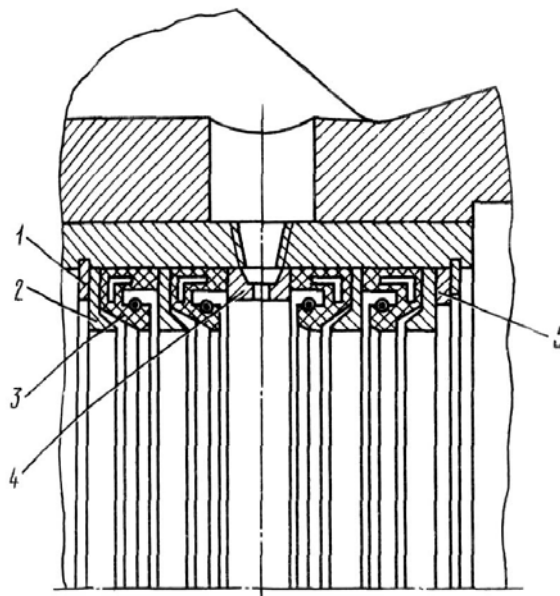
Уплотнительное устройство системы регулирования давления воздуха в шинах:
